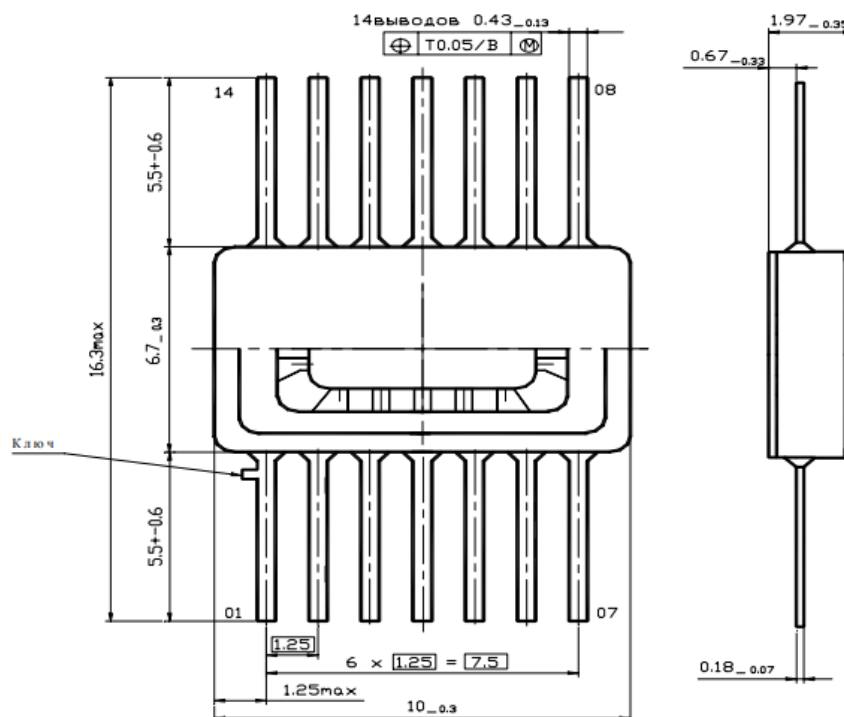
Габаритные размеры корпуса 401.14-5
